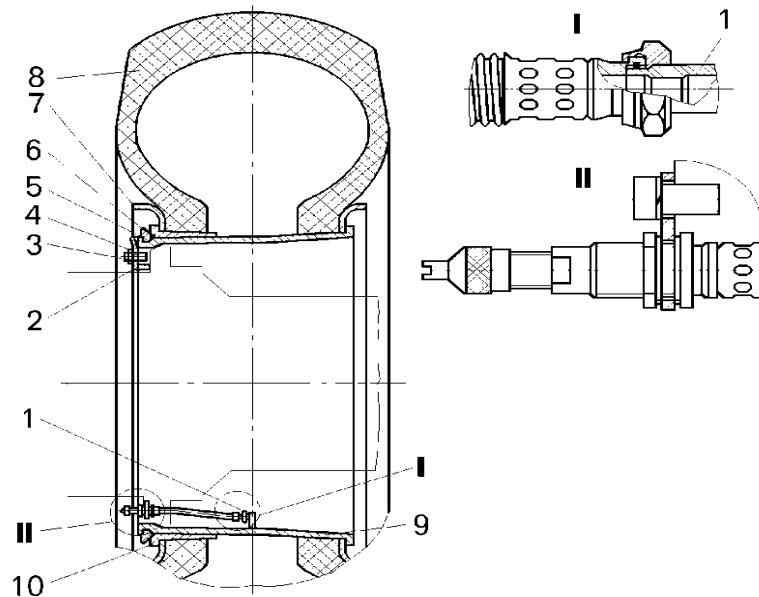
Установка переднього колеса: 1 – вентиль; 2 – притиск кріплення колеса; 3 – шпилька; 4 – гайка кріплення колеса; 5 – замкове кільце
